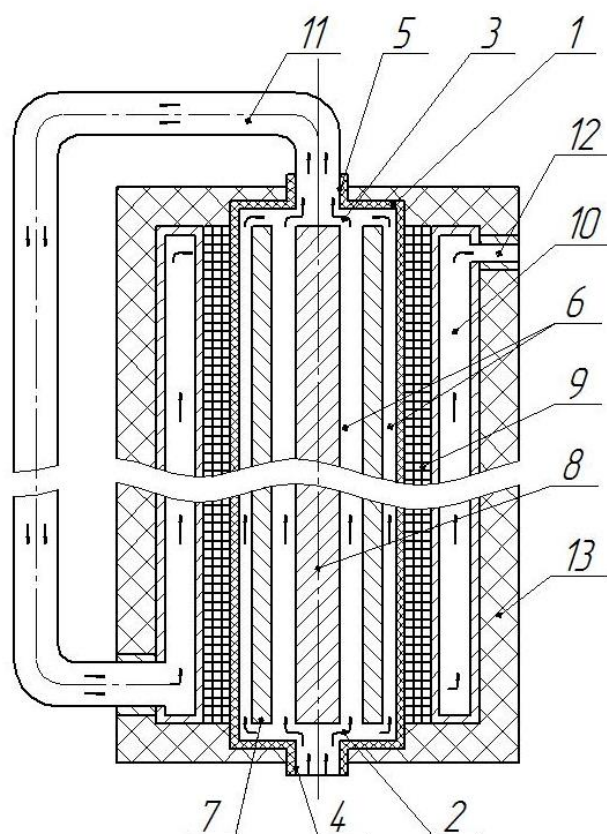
Индукционный нагреватель с выдерживателем.
